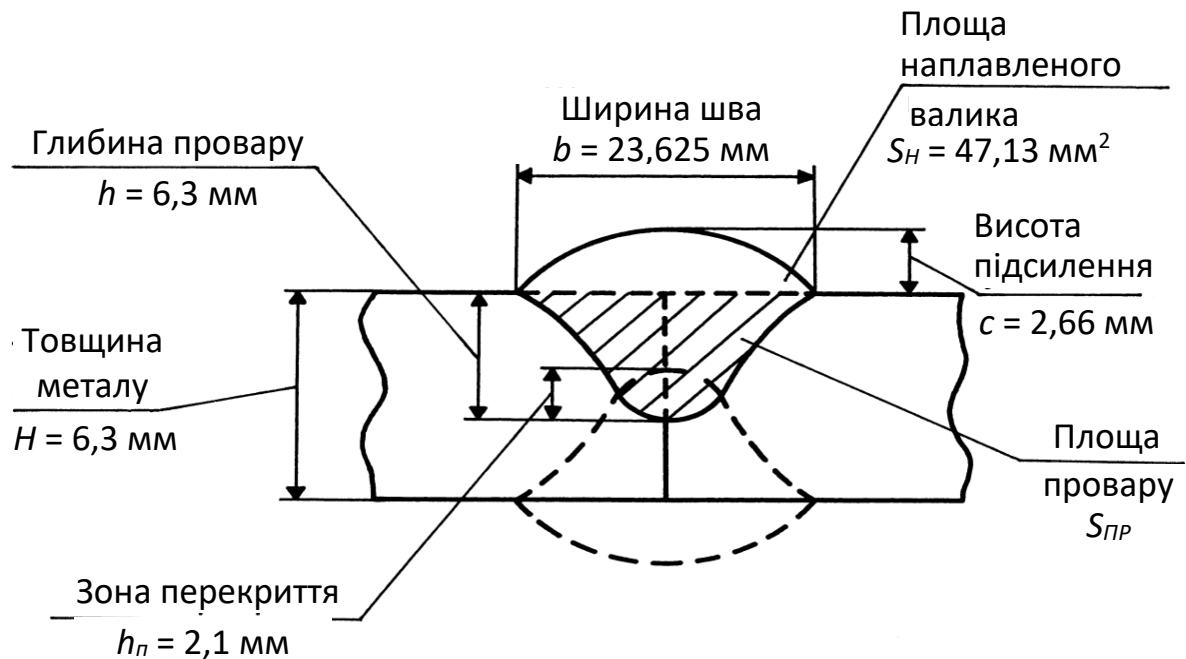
Ескіз поперечного перерізу зварного з'єднання
